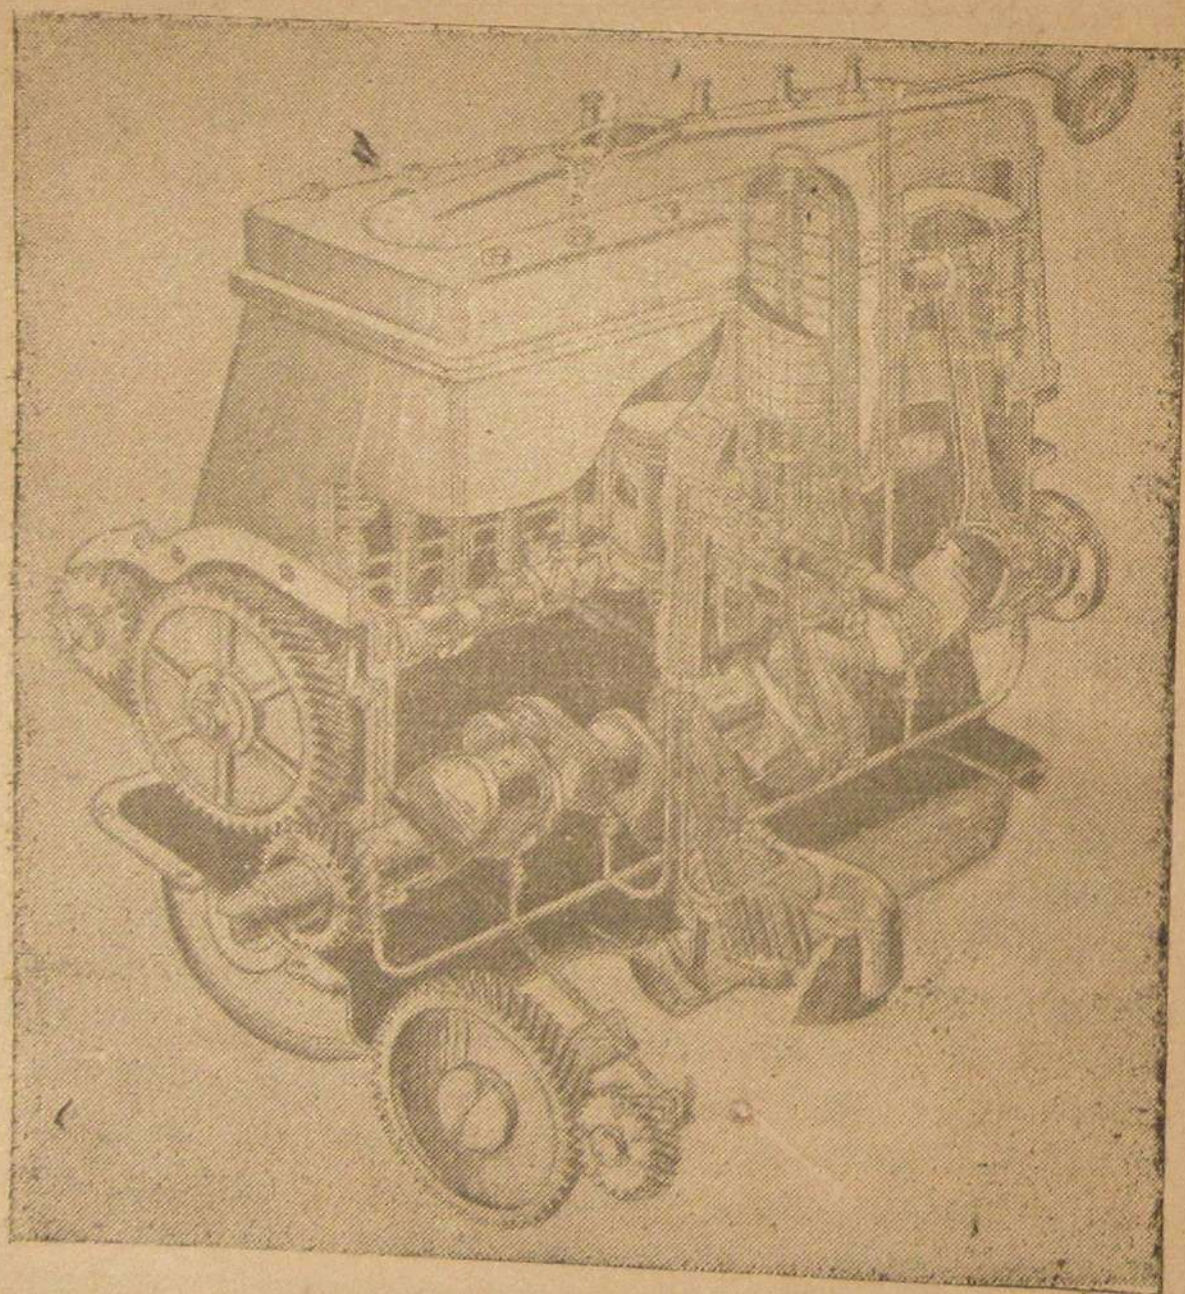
Общий вид системы смазки двигателя ЗИС-21
